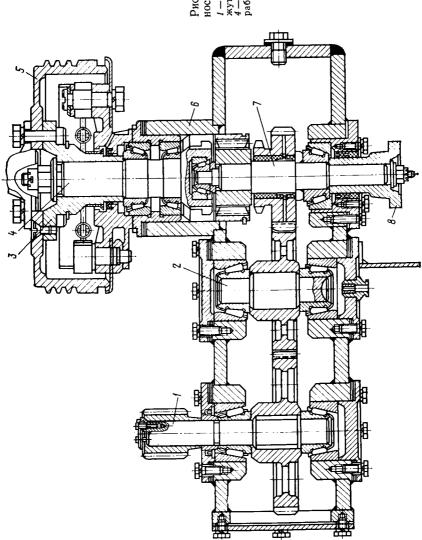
Коробка отбора мошности агрегата Азинмаш-35А; 1 — вал выводной; 2 — вал промежуточный; 3 — фланец в сборе; 4 — хвостовик; 5 — тормозной барабан; 6 — корпус; 7 — вал приемный; 8 — фланец На посту сосредоточены: педаль выключения фрикционной муфты двигателя, рычаг управления подачей топлива, рычаг управления коробкой передач автомобиля.
